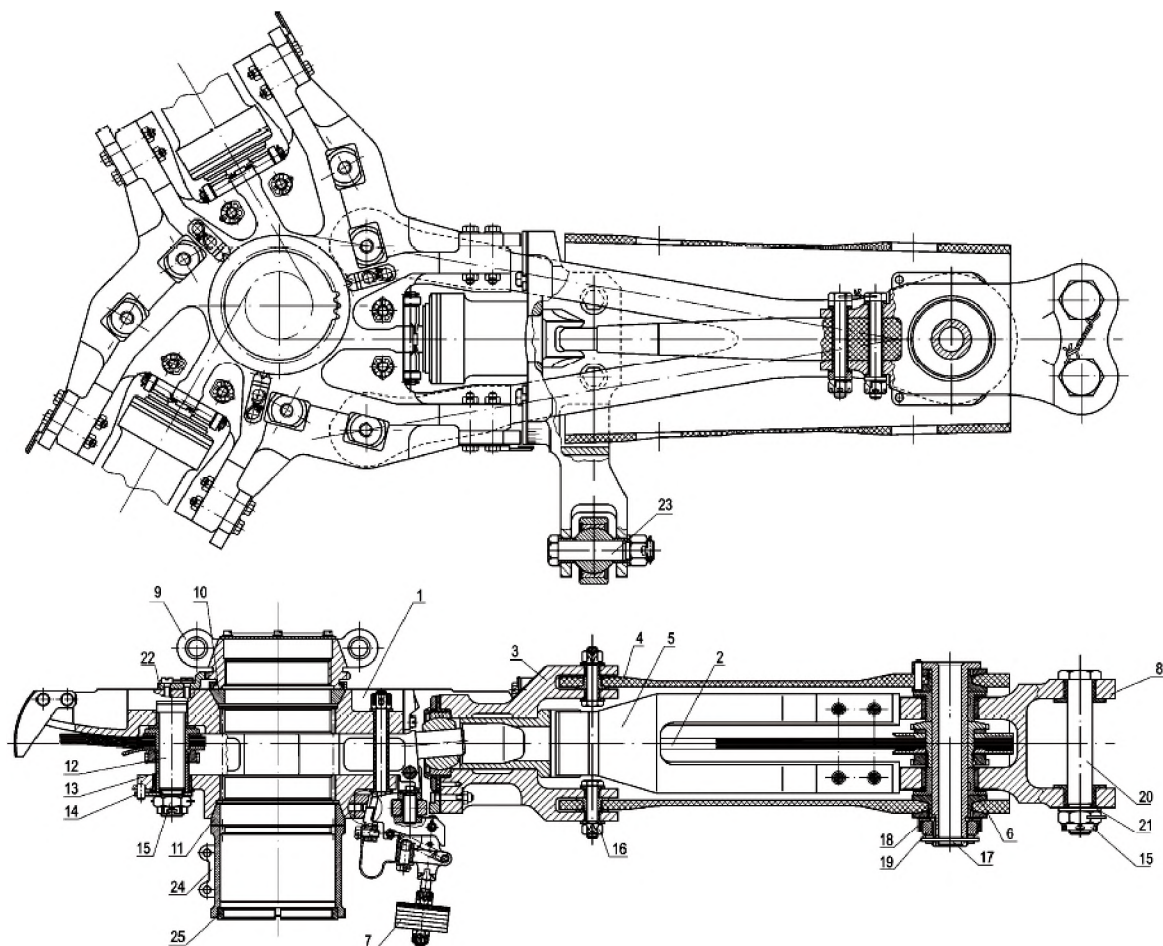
Конструкция втулки НВ Ка-226А с пластинчатым V-образным торсионом [11]:
